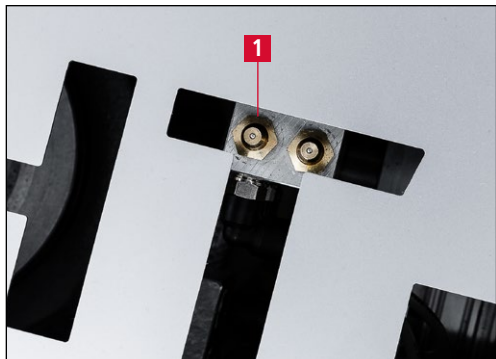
Смазочный ниппель на смазочном блоке с шариковыми одноосевыми направляющими
